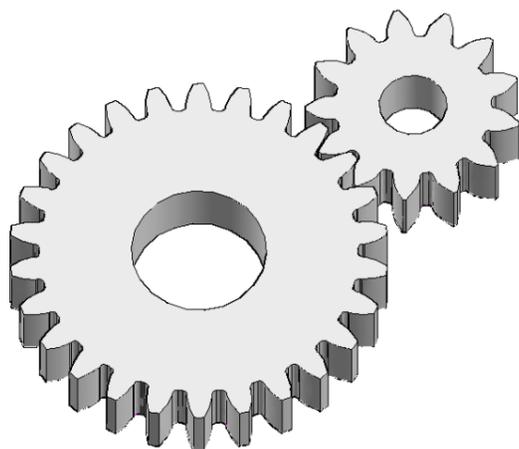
Модель зубчатого зацепления колеса и шестерни
